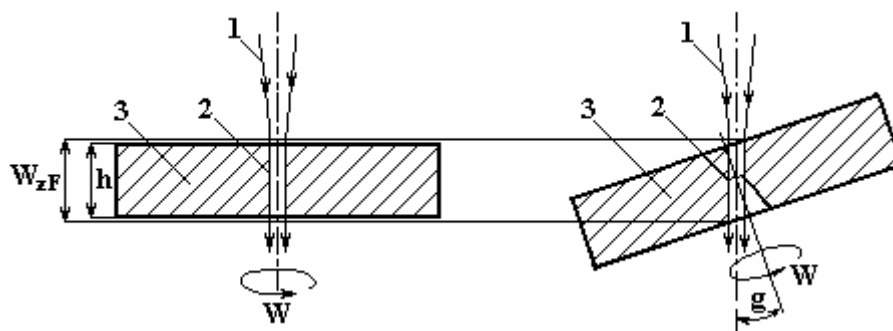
Схемы сверления отверстий во вращающейся со скоростью w заготовке толщиной h : 1 – сфокусированный лазерный луч; 2 – полость отверстия; 3 – заготовка; g – угол наклона оси вращения
